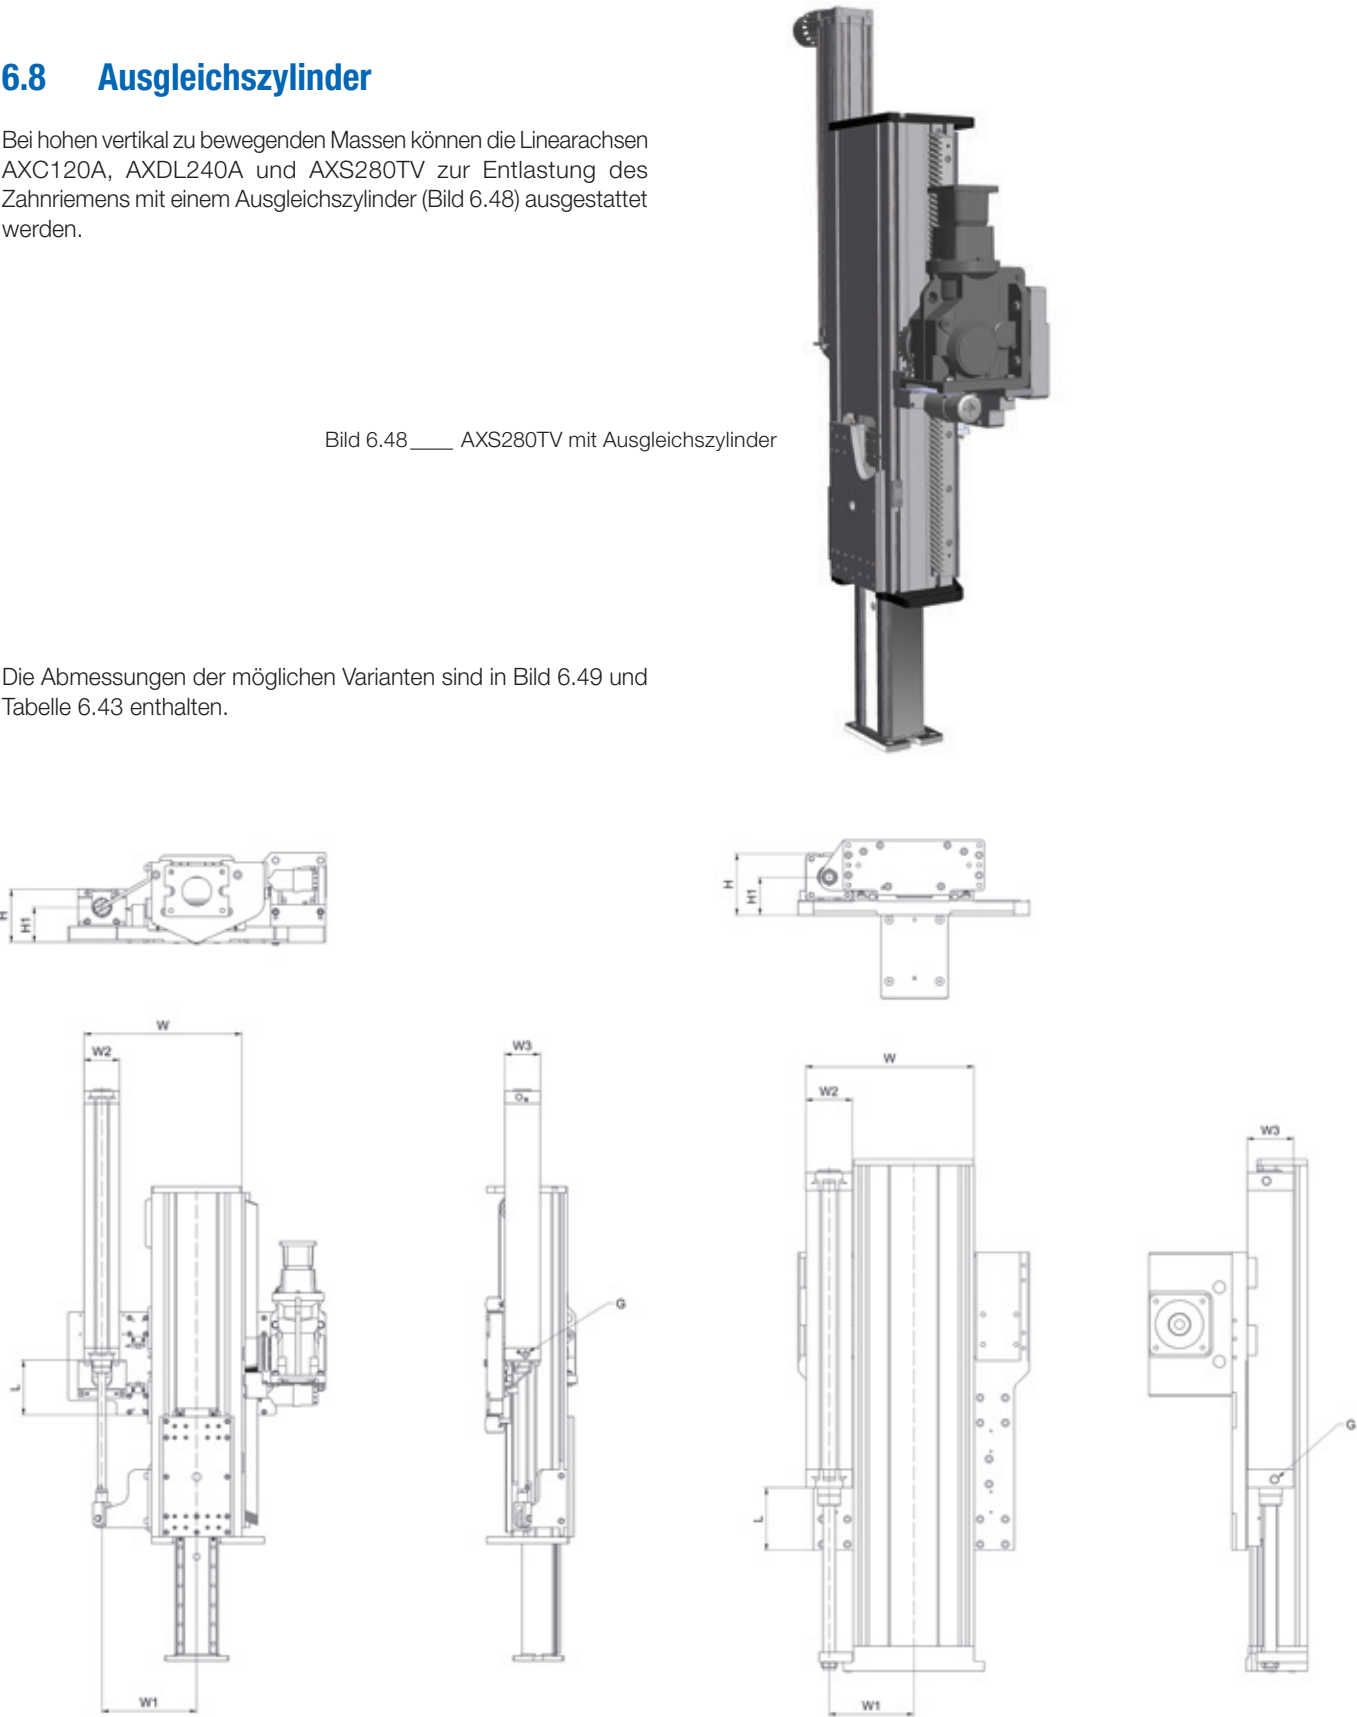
AXDL240A und AXS280TV mit Ausgleichszylinder
